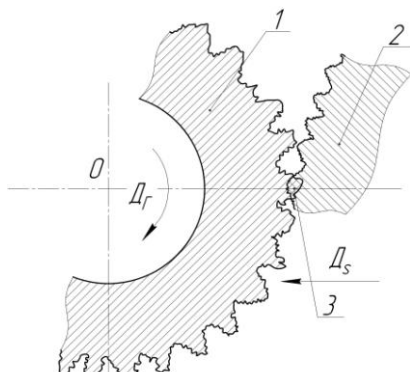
Схема адгезионного износа при скользящем точении: 1 – заготовка; 2 – режущая кромка; 3 – место холодной сварки
